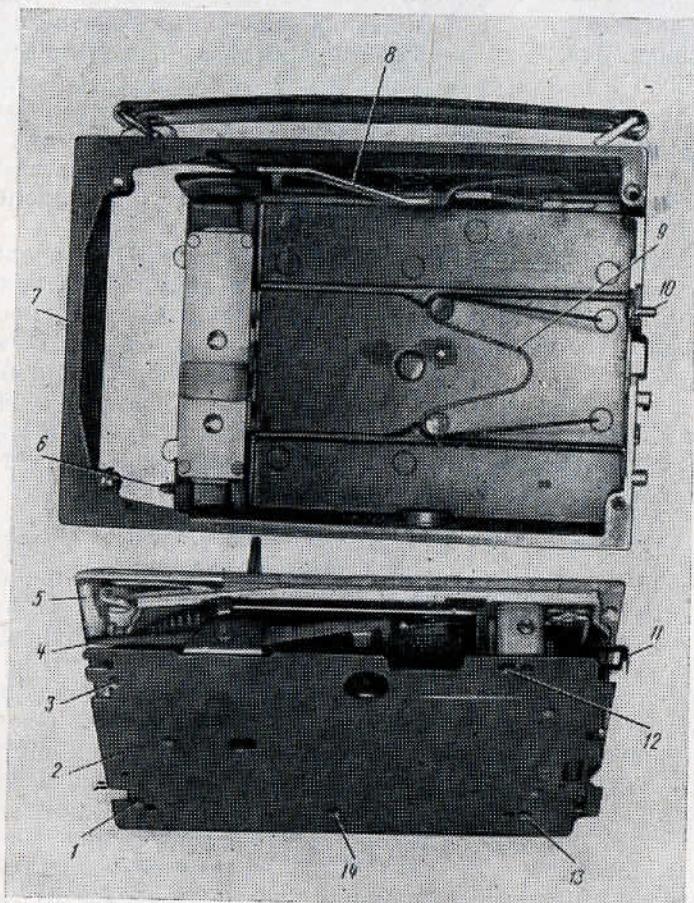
Корпус кинокамеры и монтажная стенка с механизмами:
